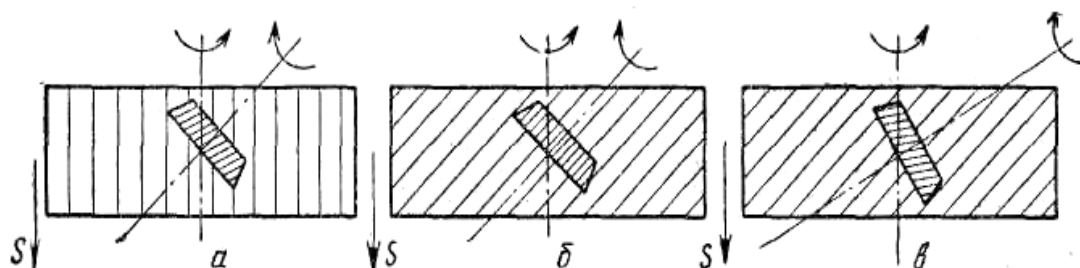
Возможные схемы зуботочения цилиндрических колес
